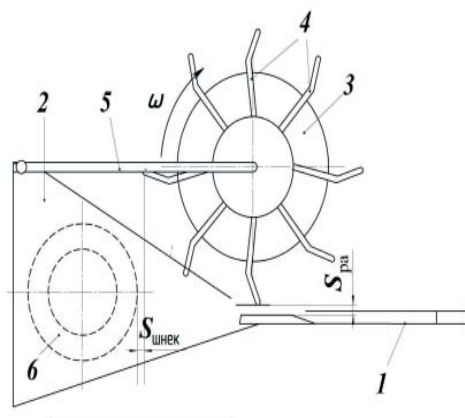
Схема параметров регулировки шнека-мотовила: 1 – стеблеподъемники; 2 – жатка; 3 – навивка шнека-мотовила; 4 – отсекатели; 5 – поддержка мотовила; 6 – шнек жатки
